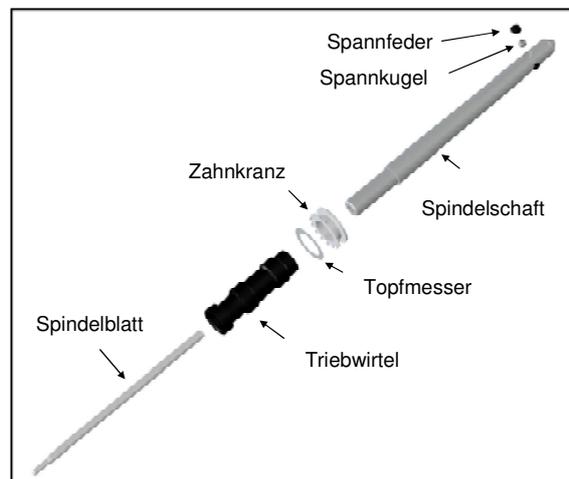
Explosionsdarstellung einer Spindel der Version 7
